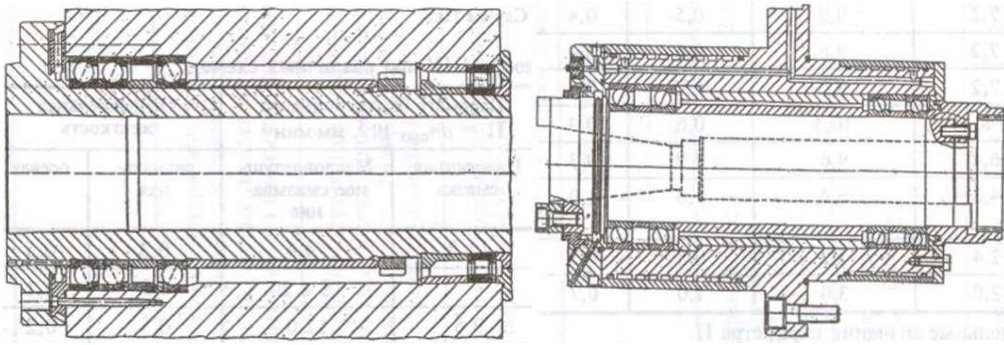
Вузол шпінделя високошвидкісного верстата типу токарного верстата «обробний центр
